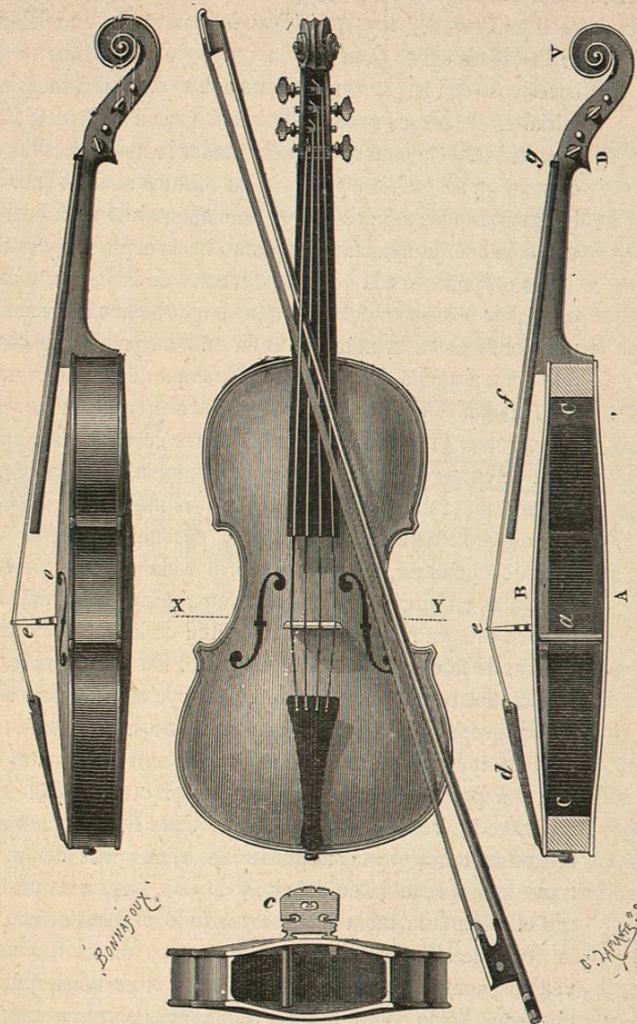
Violín: cortes longitudinal y transversal y vista de frente y de lado
